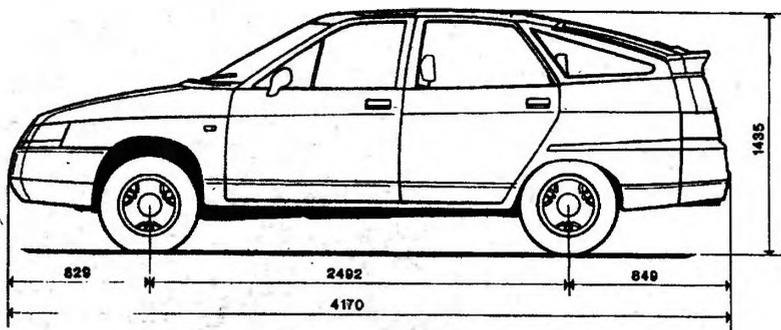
Габаритные размеры автомобиля ВАЗ-2112
